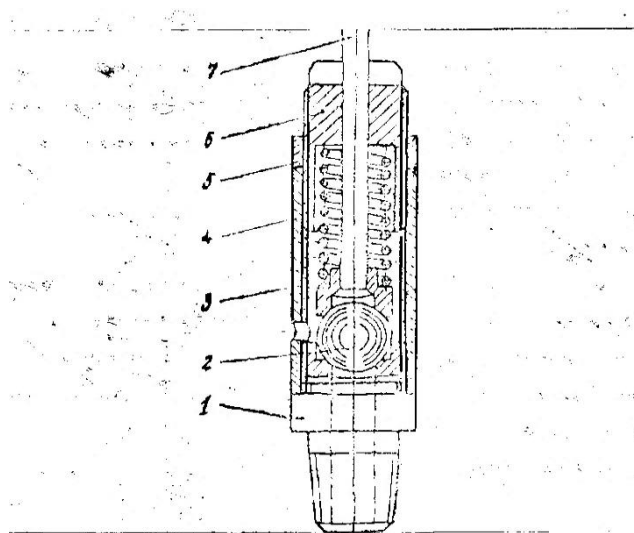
Предохранительный клапан: 1 – седло клапана; 2 – клапан шариковый; 3 – корпус; 4 – пружина; 5 – контргайка; 6 – винт регулировочный; 7 – стержень
